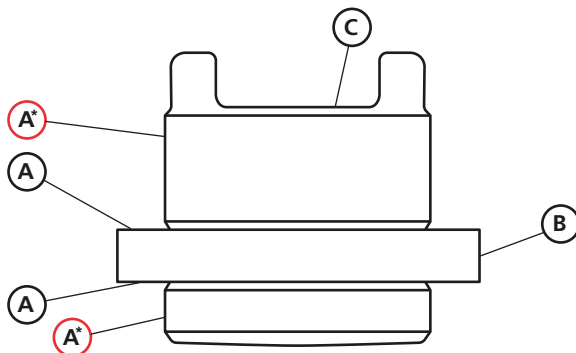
Douille d'entraînement HOB3, surfaces importantes
